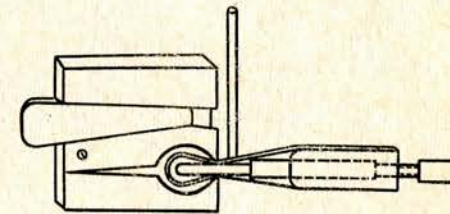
Склеивание фильца в кламере: 1 — кожаный ремень; 2 — металлический штифт; 3 — колодки (зажимы); 4 — обойма; 5 — фильц; 6 — керн
